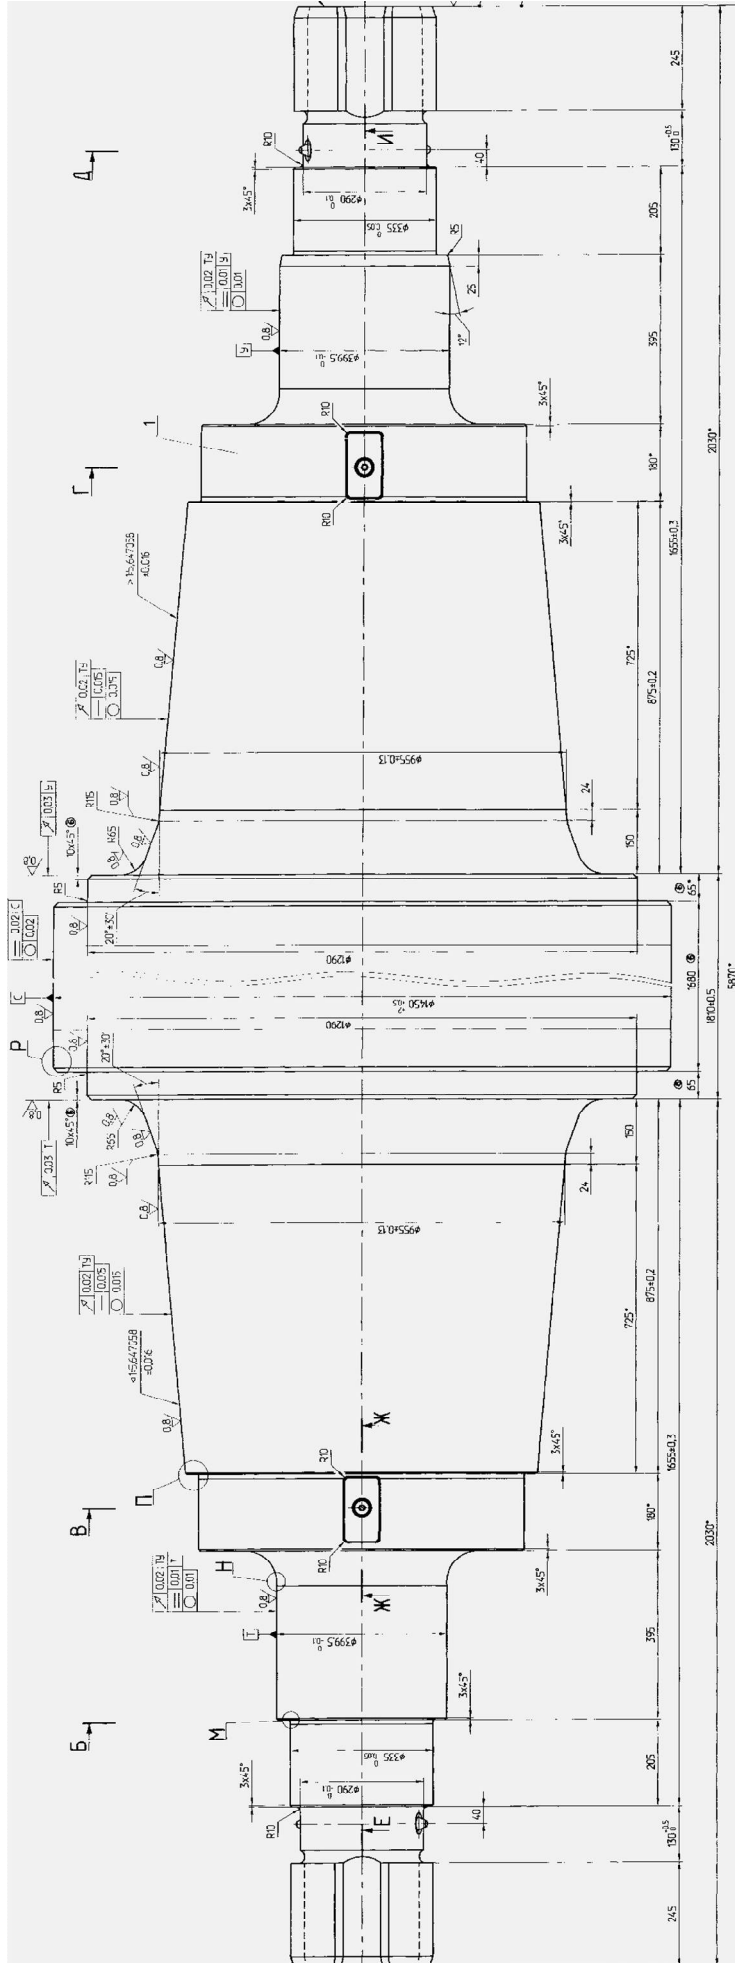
Чертёж опорного вала горячей прокатки 672с – 242
